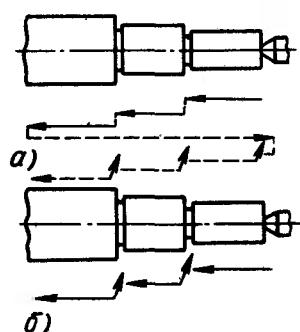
Схемы чистовой обработки ступенчатых валов
